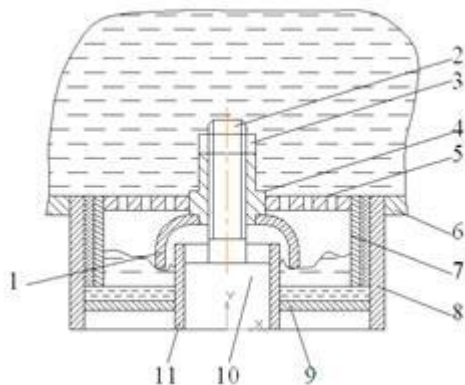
Установка колпачка: 1 – колпачок; 2 – шпилька; 3 – гайка; 4 – втулка; 5 – ситчатый диск; 6 – тарелка; 7, 8 – обечайки; 9 – диск; 10 – полоска; 11 – патрубок
